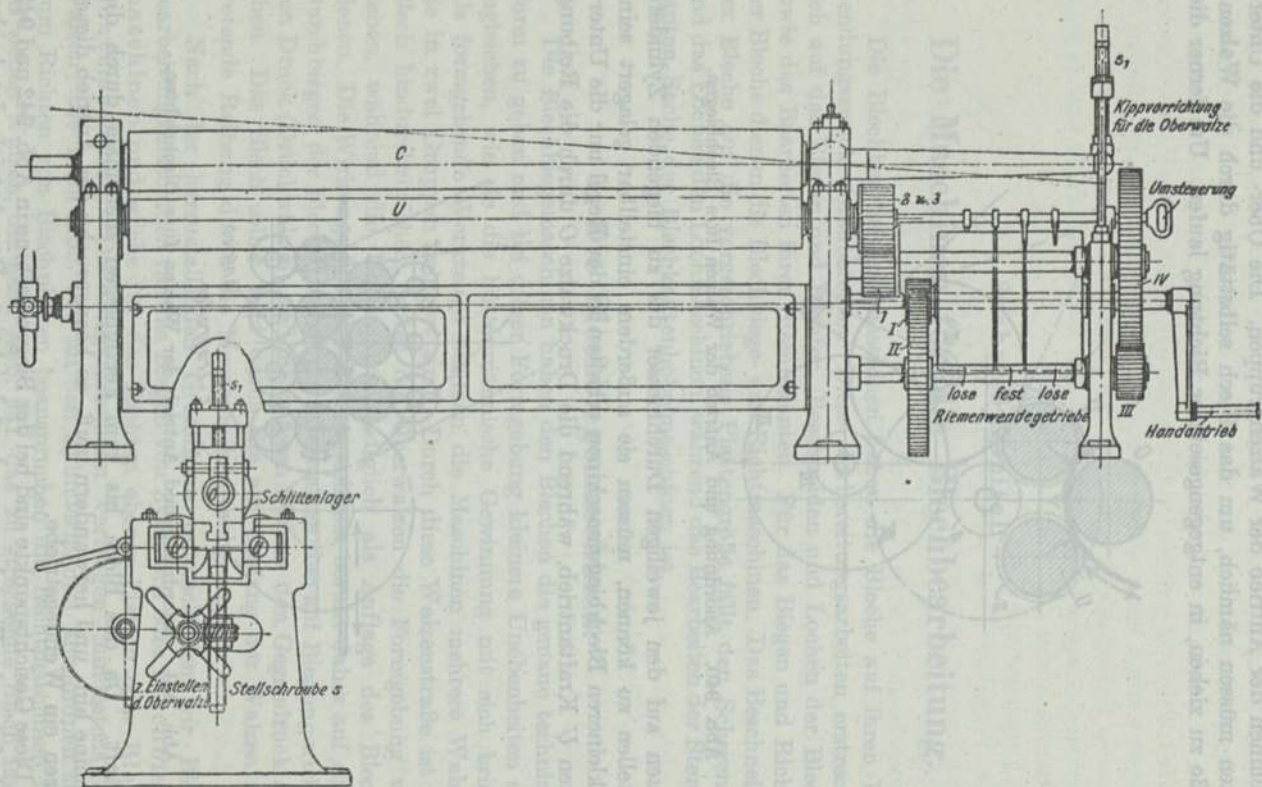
und 943. Blechbiegemaschine. Dampfkessel- und Gasmotorenfabrik, Braunschweig.
